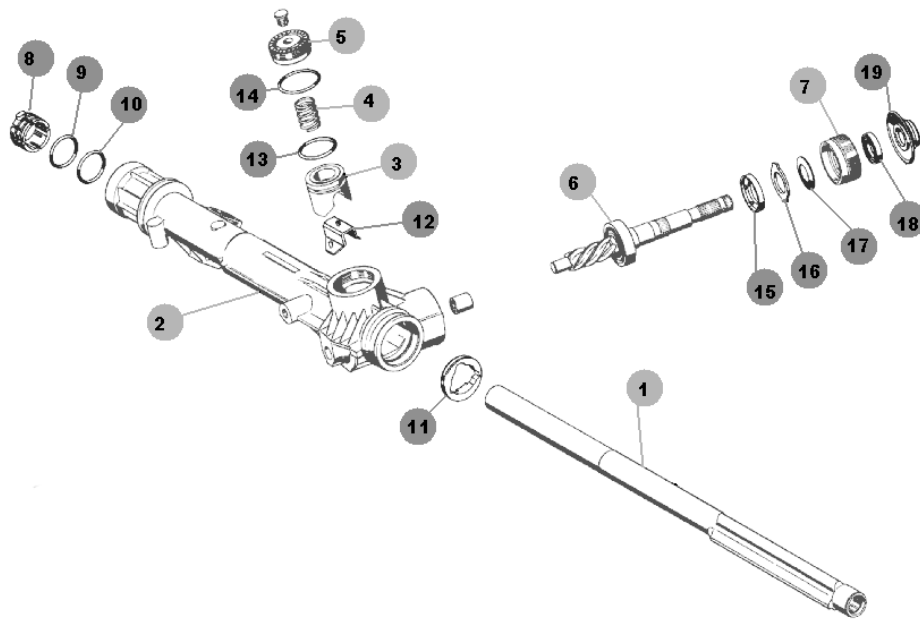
Конструкція механічної рульової рейки 1-й вид:
